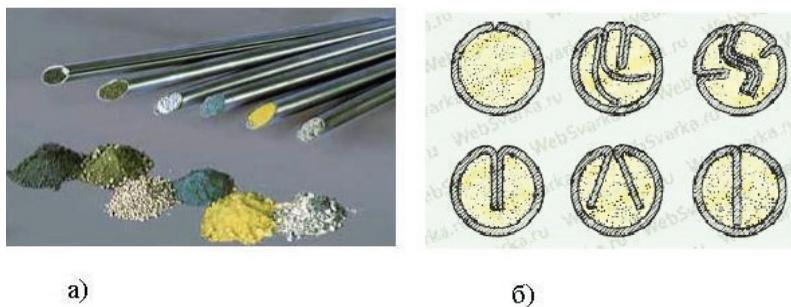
Порошковые проволоки для сварки и наплавки:
